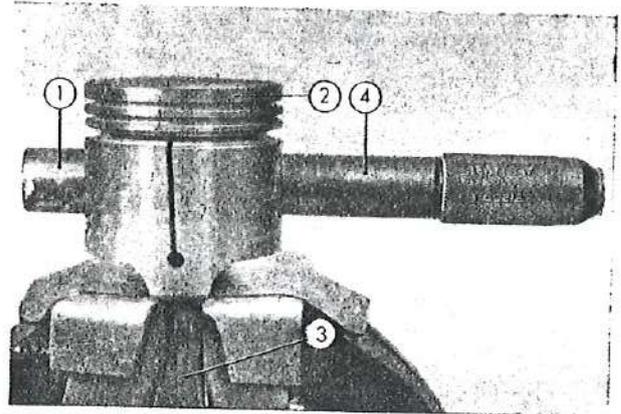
Desmontaje del bulón mediante el útil A.60212.
